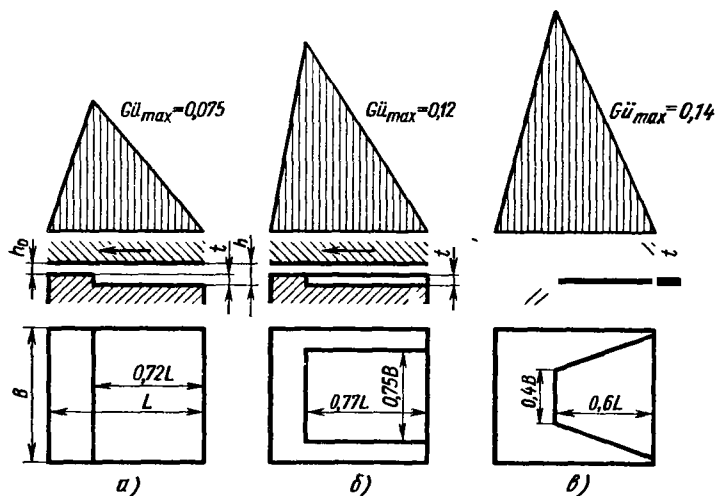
Подшипники со ступенчатыми несущими поверхностями
